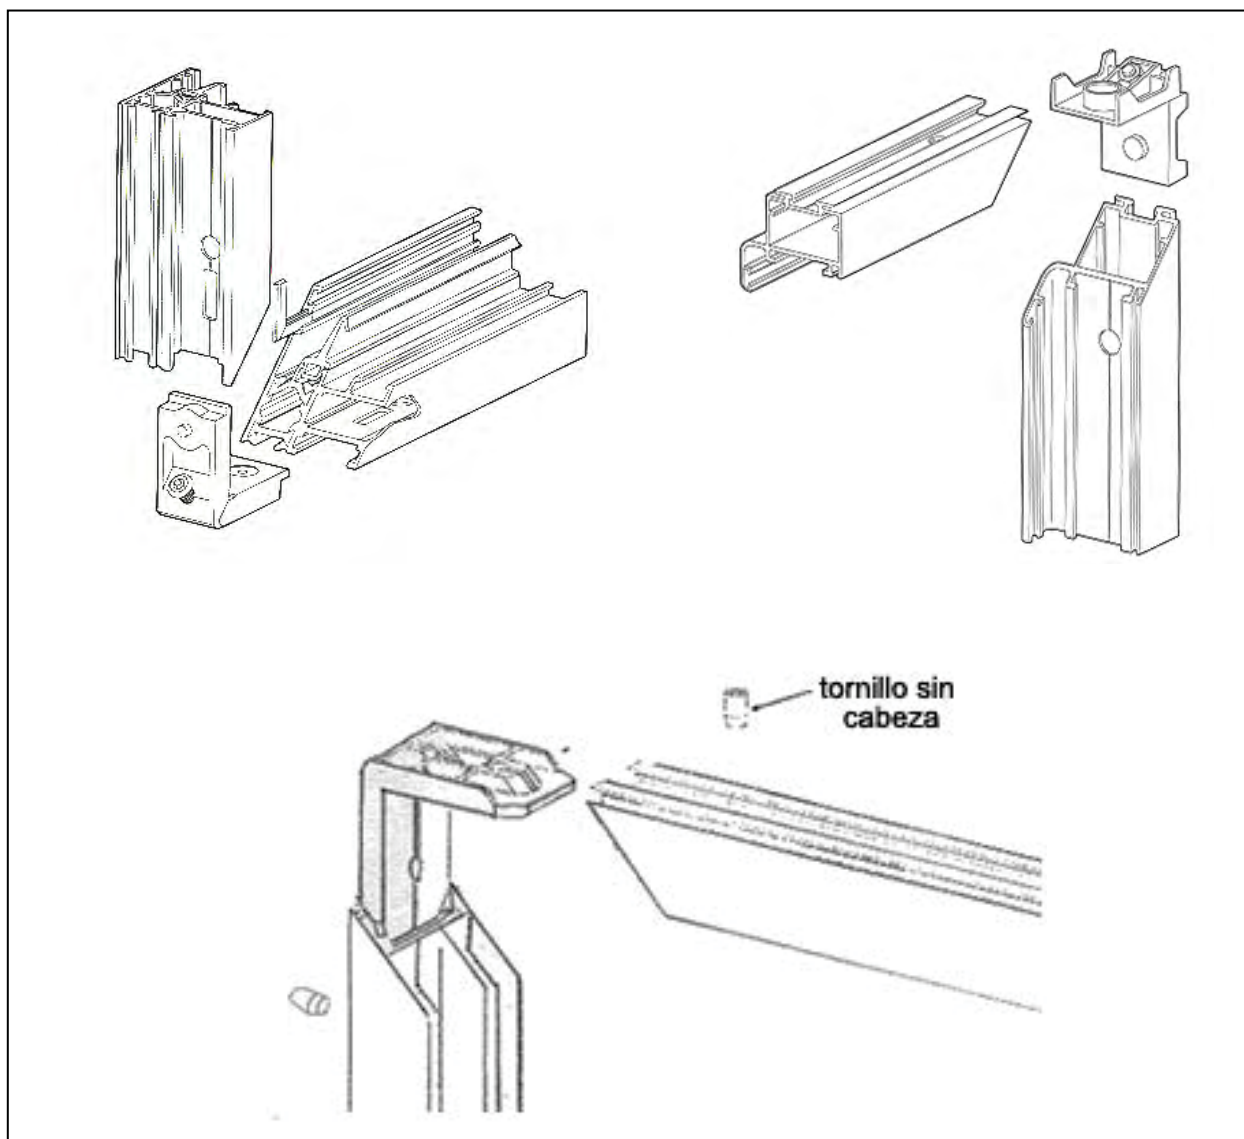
DETALLE DE ENSAMBLE DE PERFILES DE ALUMINIO EN ESQUINA
